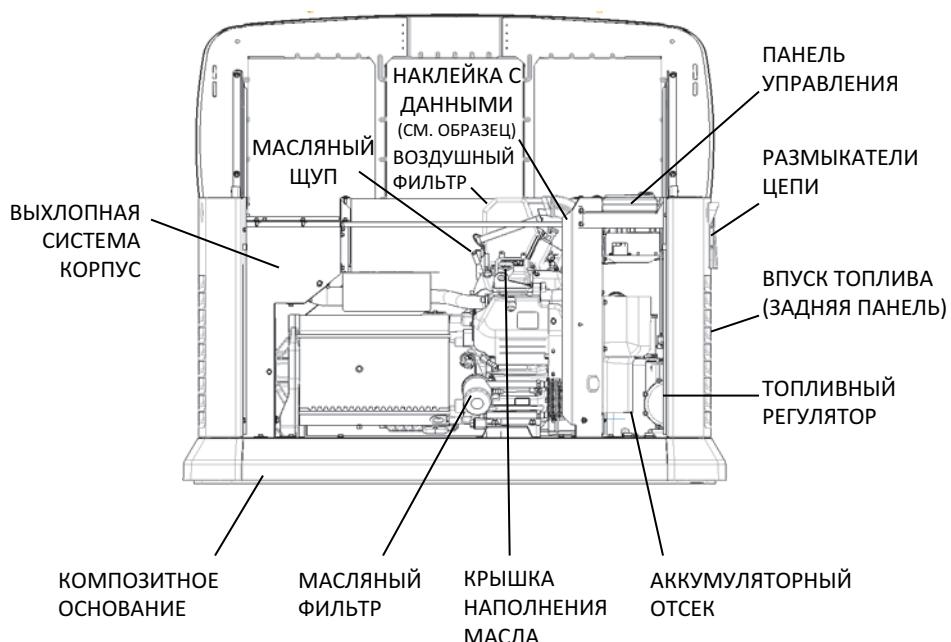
Двигатель GT-990, блок 10 и 13 кВА
